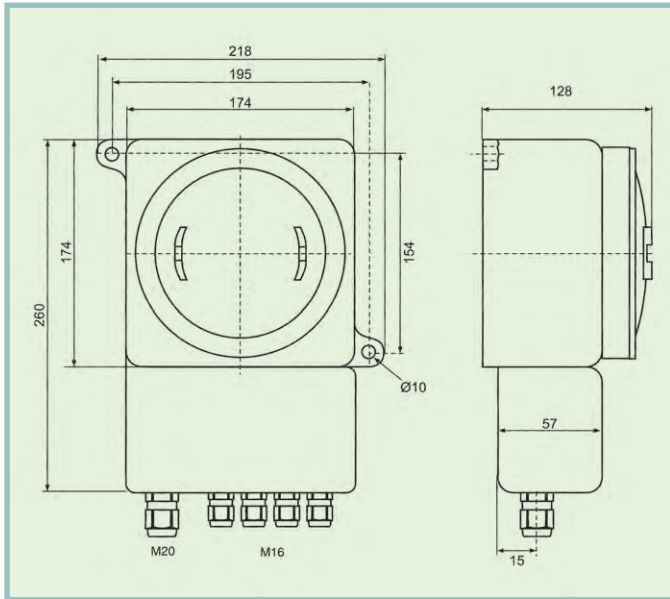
Габаритный чертёж источника питания RSxx-PSD-Ex4.34
